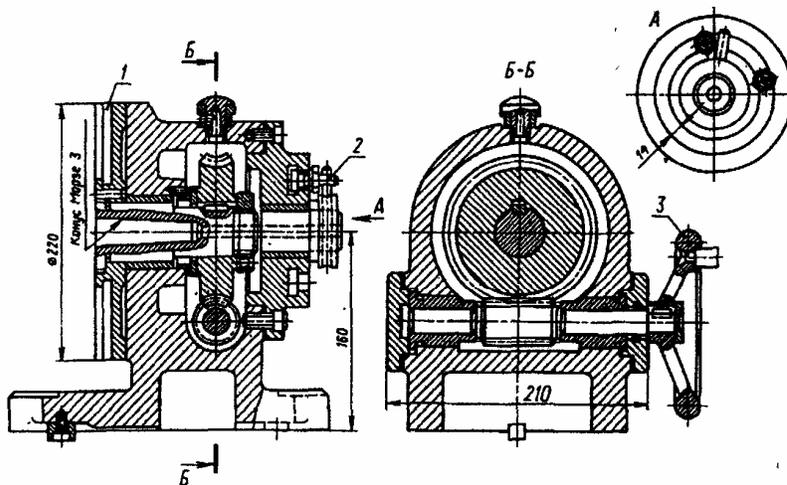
Поворотный стол для фрезерования по радиусу
